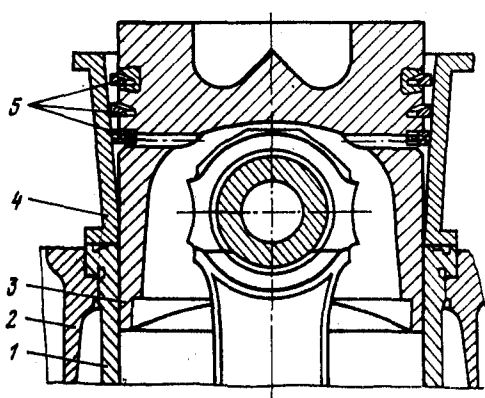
Приспособление для установки поршня с кольцами в цилиндр:
